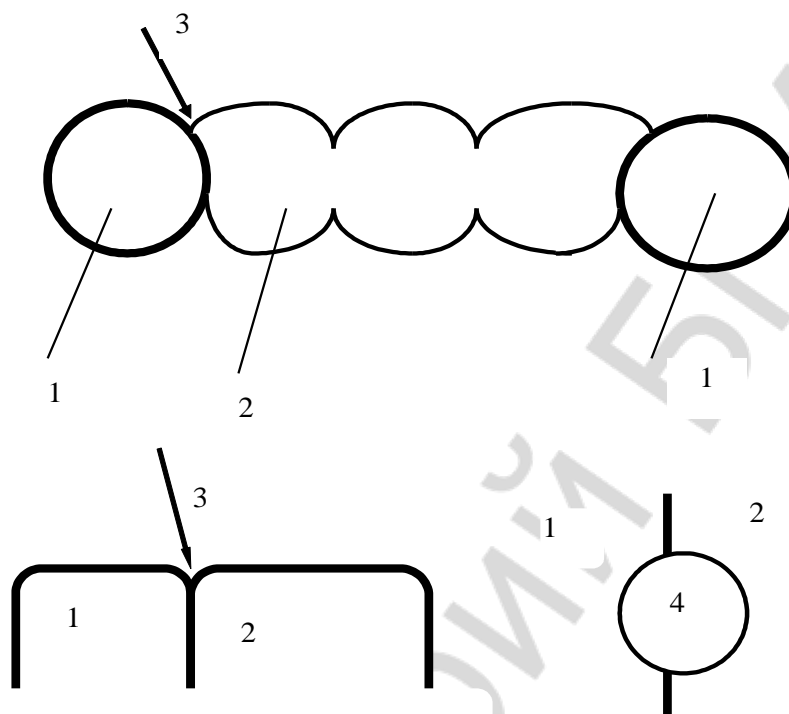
Направление и фокусировка лазерного луча при лазерной сварке опорной коронки и промежуточной части мостовидного протеза:
